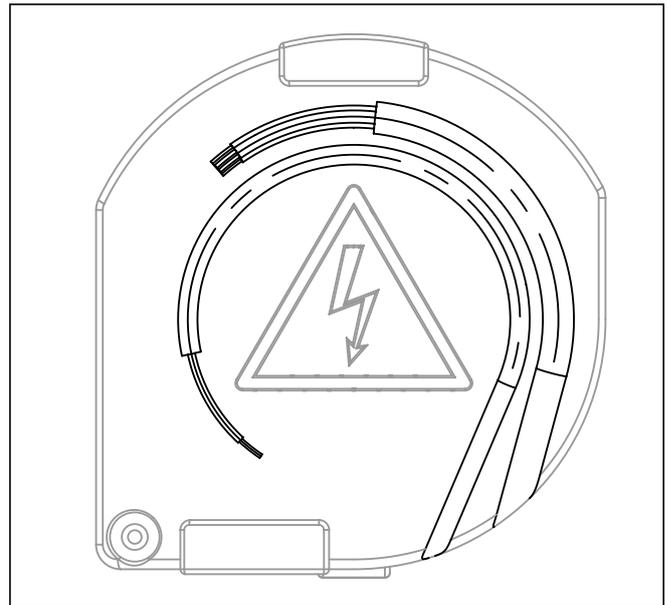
Flanschisolierung mit Schablone zum Ablängen der Kabel
